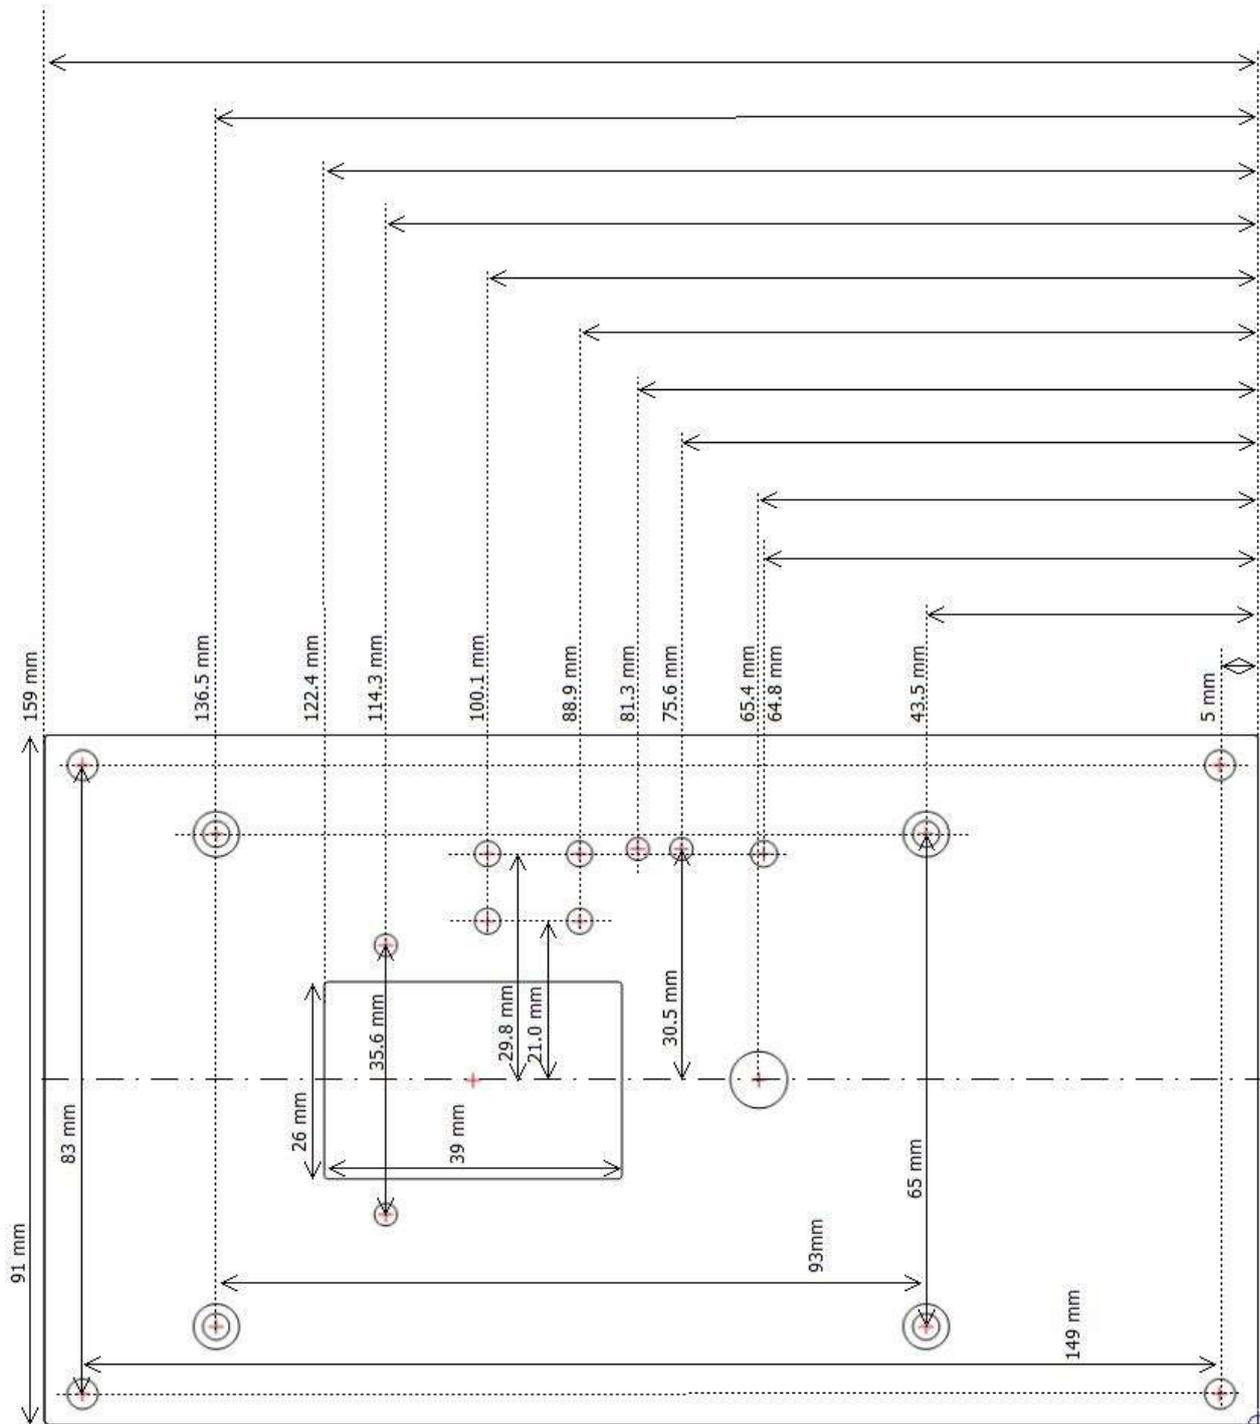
Maßzeichnung Frontplatte für Teko 103 Gehäuse
